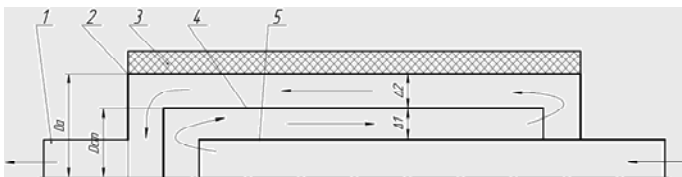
Конструктивная схема электромагнитного аппарата: 1 – отводящий патрубок; 2 – корпус; 3 – обмотка, 4 – стакан; 5 – подводный патрубок
